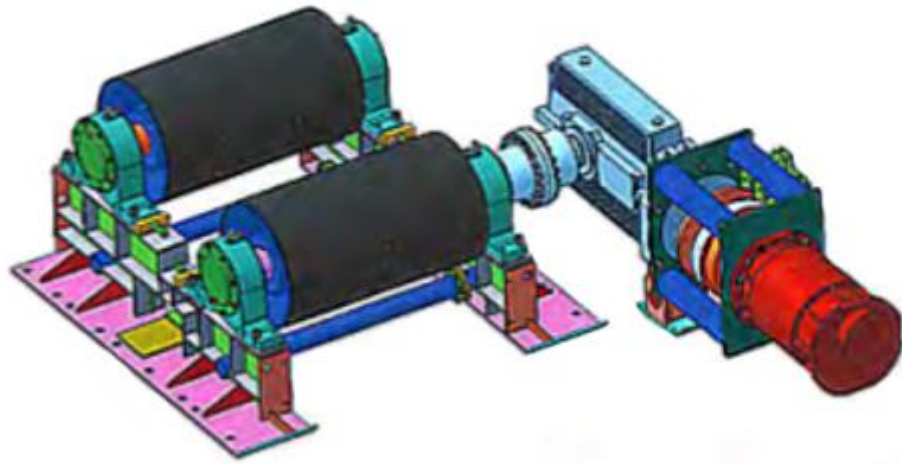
Двухбарабанный привод с цилиндрическим редуктором
